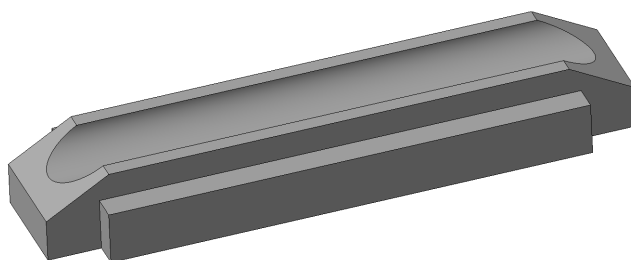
Общий вид конструкции токоъемника по патенту [6]
